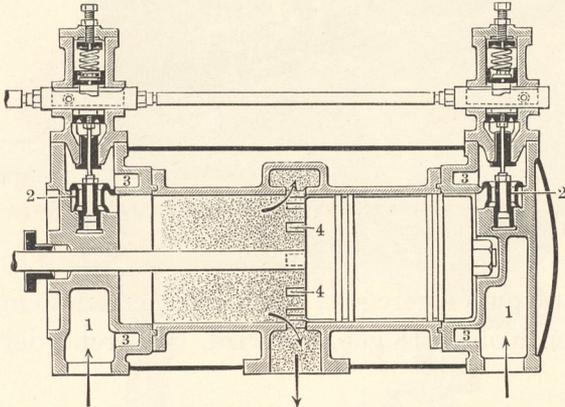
Zylinder der Gleichstromdampfmaschine.
